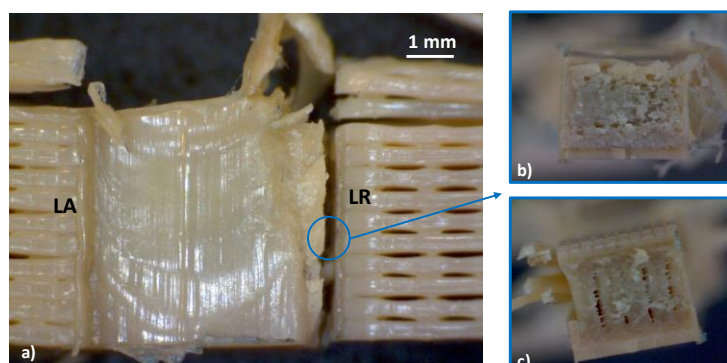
Macrografia do provete com pior valor de ERJS após Ensaio 3: a) Superfície superior do provete, b) Superfície de fratura do cordão de soldadura do LR, c) Superfície de fratura da interface do material base com o LR.
